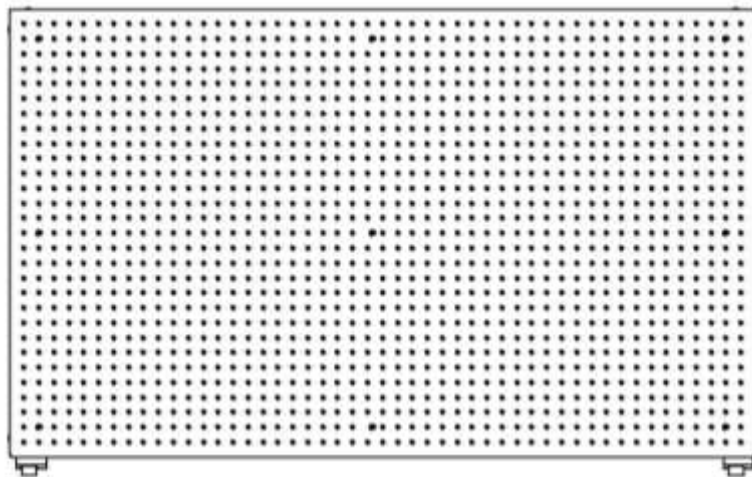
Загальний вигляд стола зварювального пересувного
